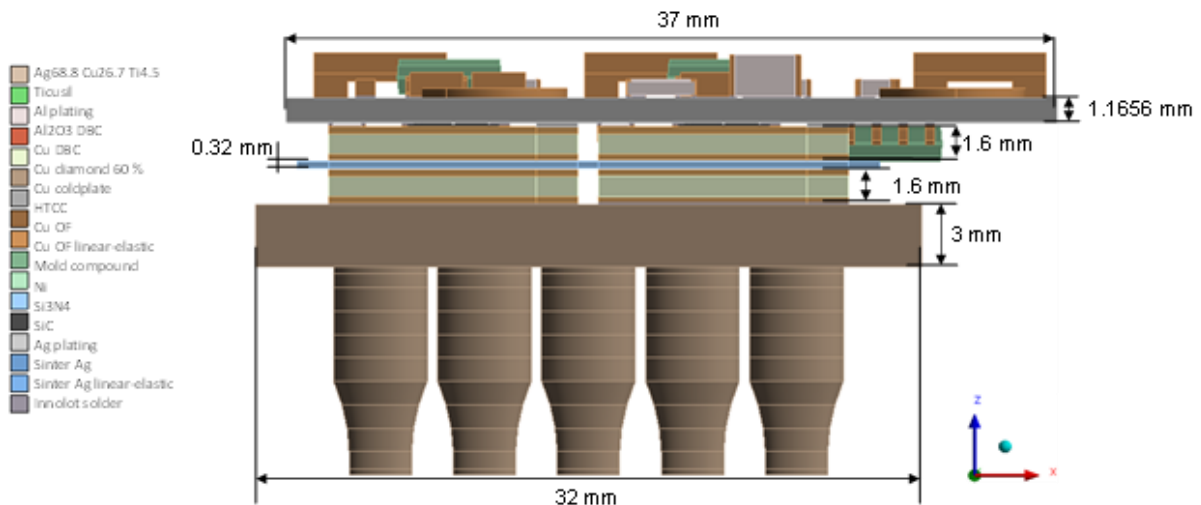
Finale vereinfachte CAD Geometrie des SiCool Demonstrators für den digitalen Zwilling mit Abmessungen in der Seitenansicht.
